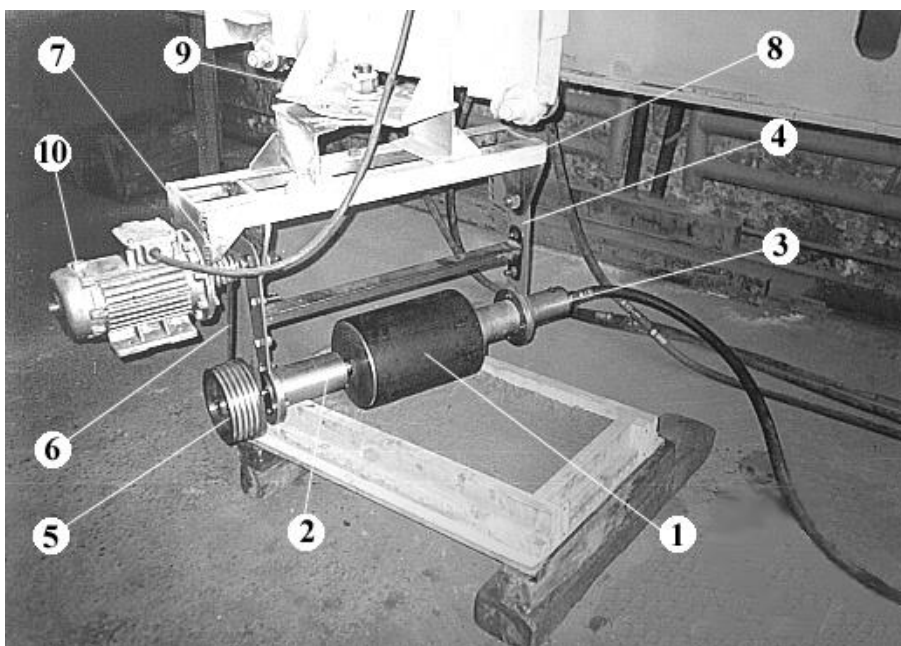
Валковый рабочий орган с приводом поперечных колебаний
